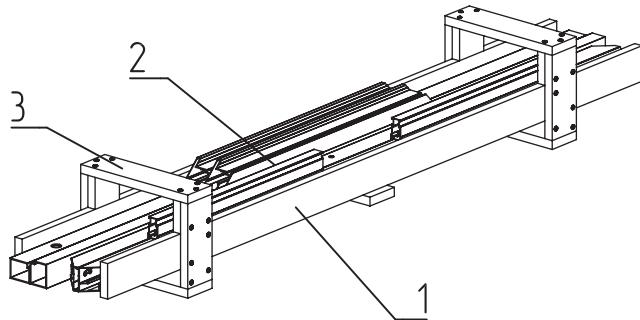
Упаковка деталей рамы калитки (FLGU.400.9803)
